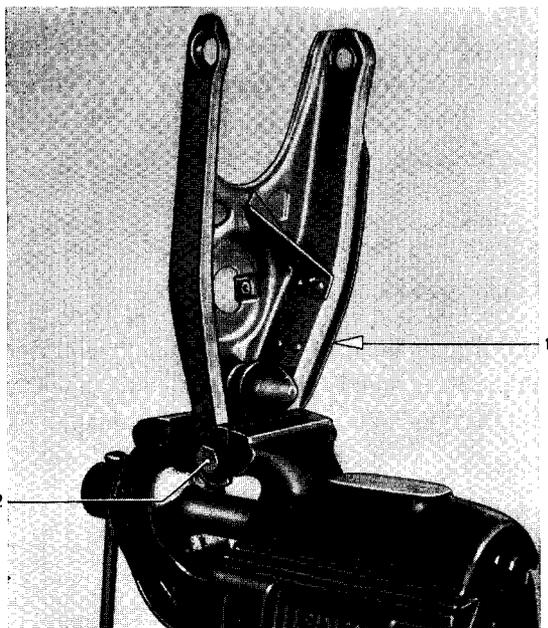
Unteren Lenker zum Heraus-schrauben der Gewindebuchsen für Querstück in Schraubstock gespannt
